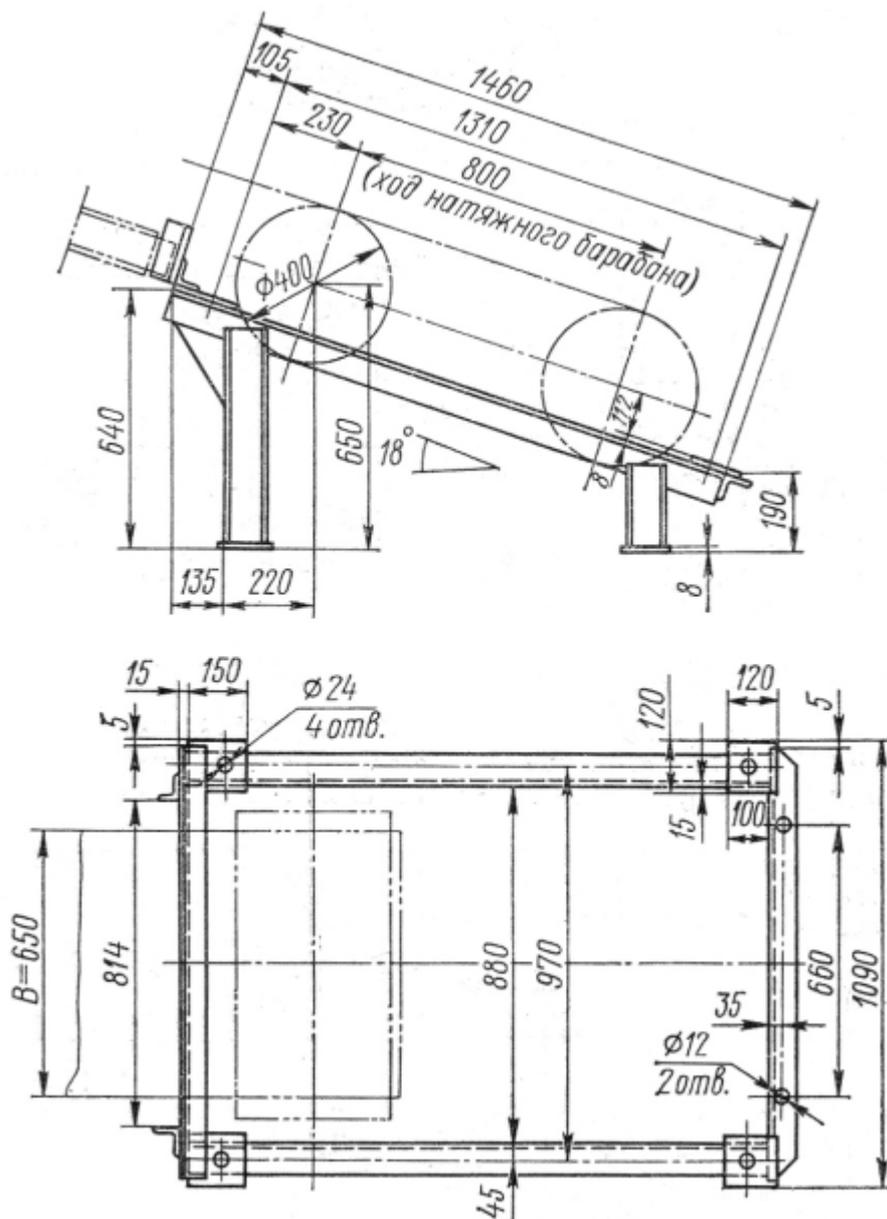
Пример конструкции опоры винтового натяжного устройства ленточного конвейера с шириной ленты 650 мм
